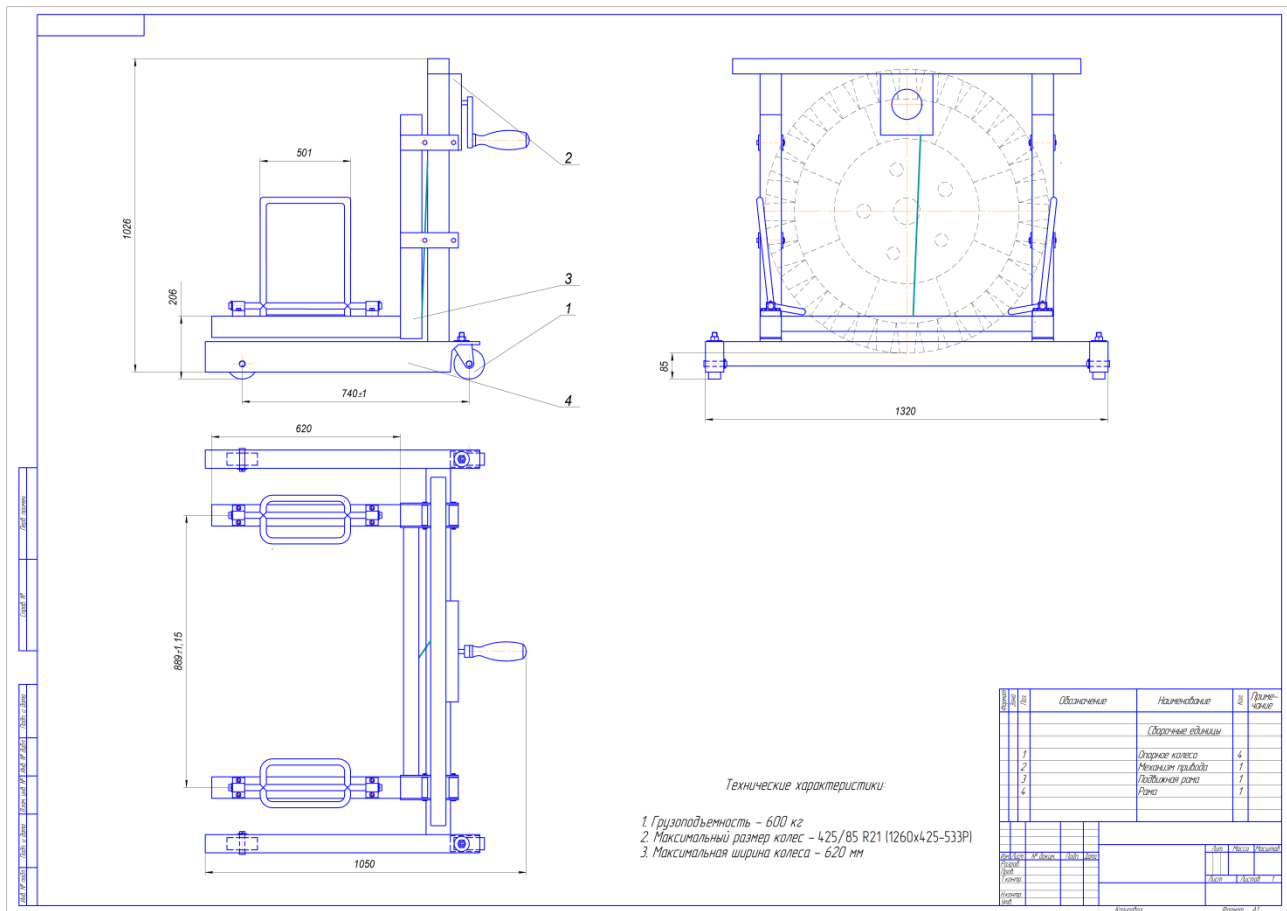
Тележка для монтажа/демонтажа колес автомобилей. Вид общий
